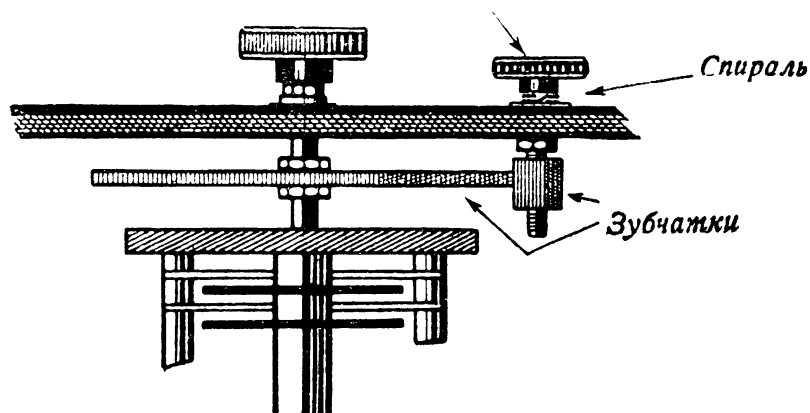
Приспособление для прецизионной установки обычного вращающегося конденсатора.
